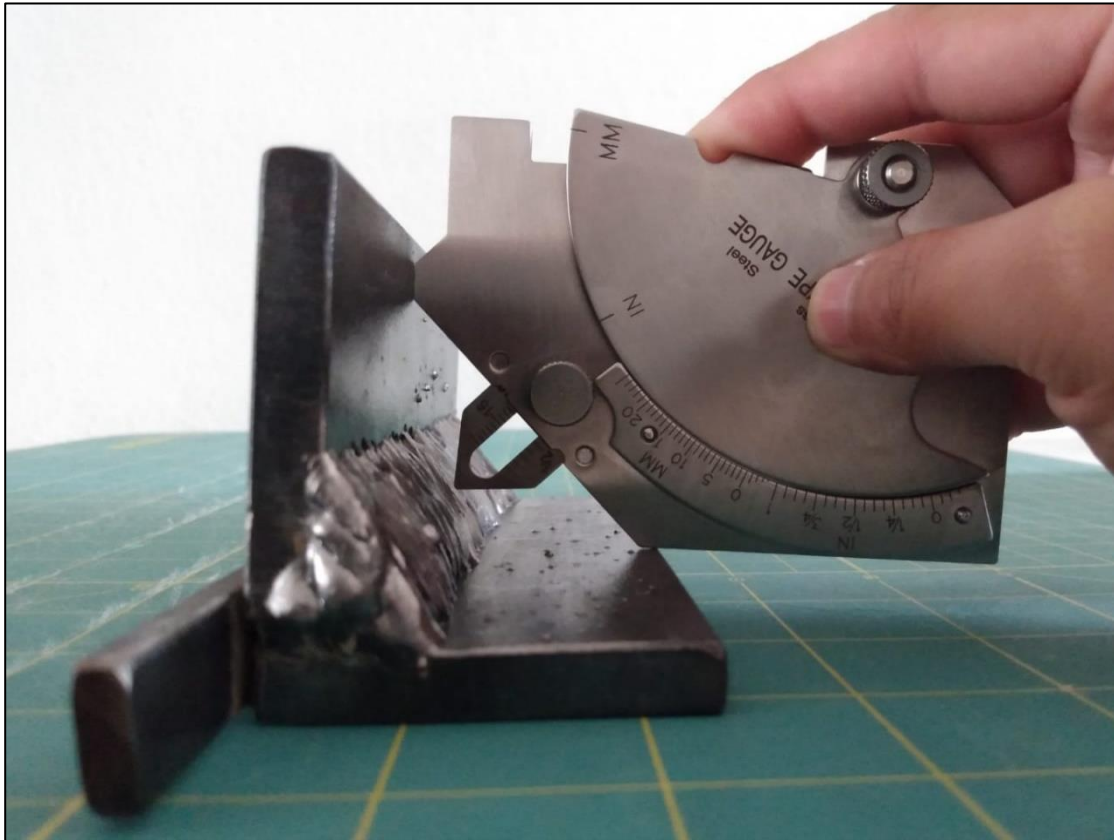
Medición De La Garganta Real De La Soldadura De Filete [64].
